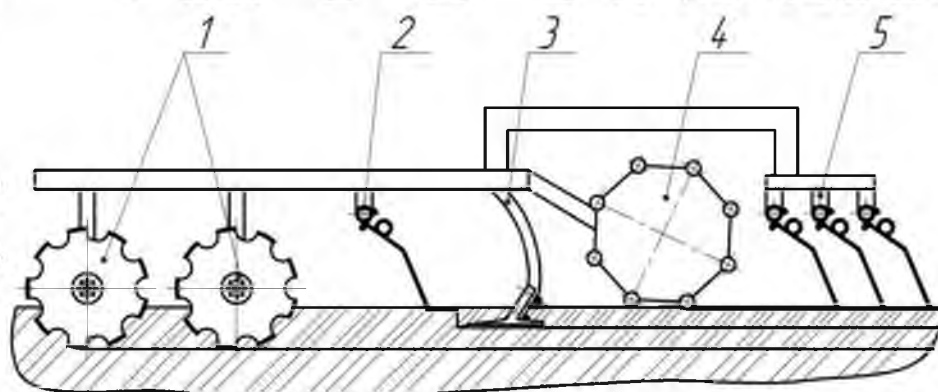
Комбінований дискокультиватор АДК фірми "Техмаш": 1 - сферичні диски; 2 - пружинна борона; 3 - культиваторна лапа; 4 - коток; 5 - трирядна пружинна борона
